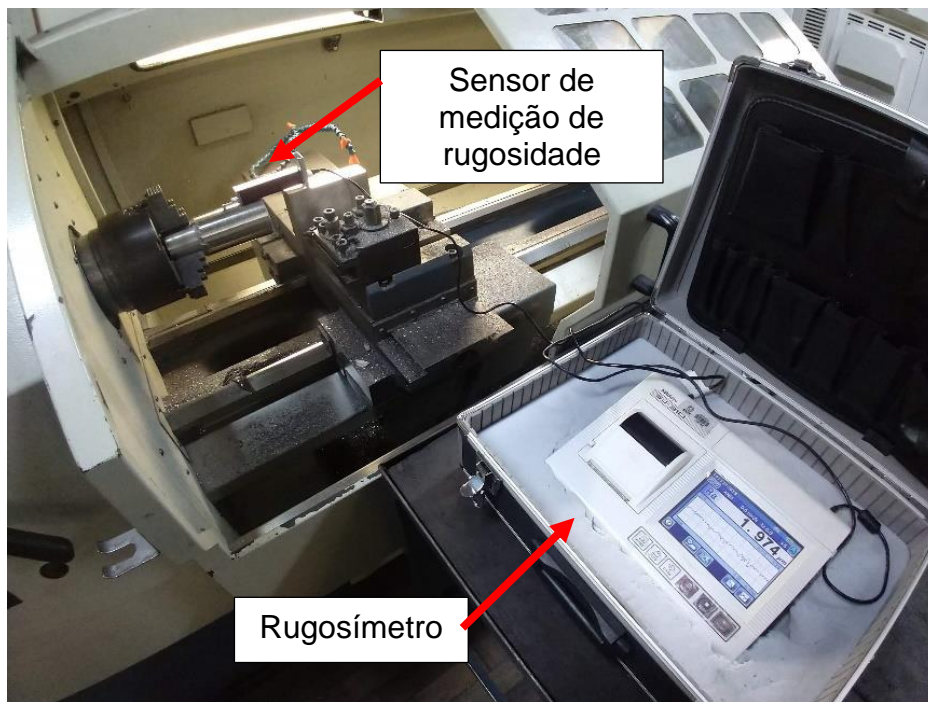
Rugosímetro Portátil SurfTest SJ-310, Fabricante MITUTOYO
